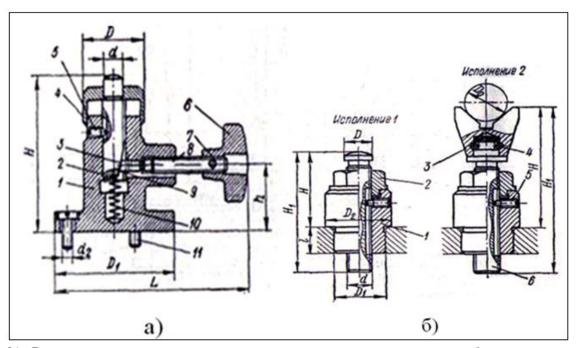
Вспомогательные опоры: а – регулируемая, самоустанавливающаяся; б – винтовая подпорка На рис. 2.31, *а* показана конструкция такой опоры. При установке заготовки в
